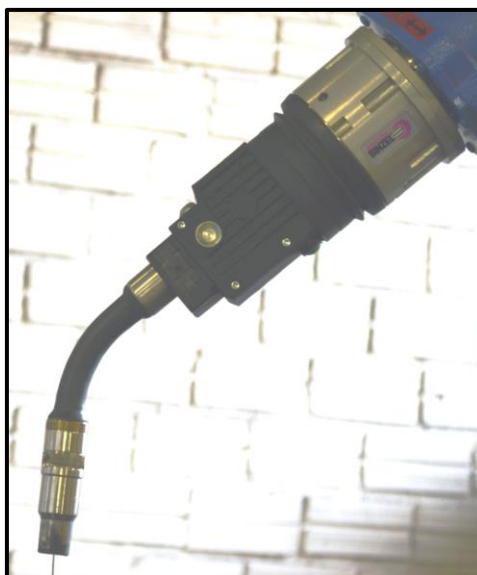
Manipulador iCAT e tocha de soldagem MIG/MAG instalados no órgão terminal do robô.
